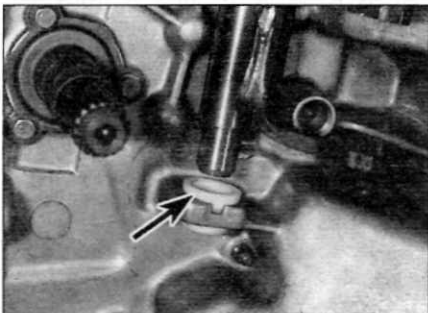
, б. ...затем высвободите вал из нижней втулки (отмечена стрелкой) и выведите его из штатного положения (коробки передач MA5 и BE3/5)
